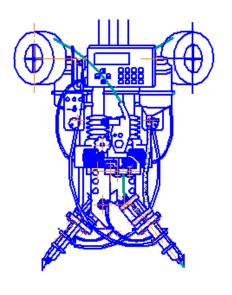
Сварочный автомат АДГ-630
